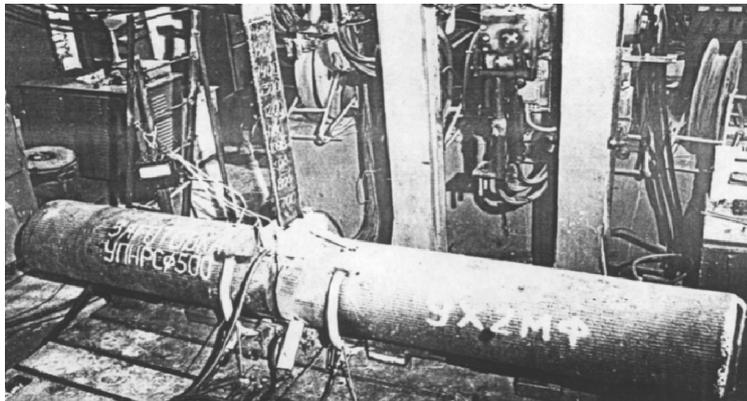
Заготовка типа вала, собранная под электрошлаковую сварку
